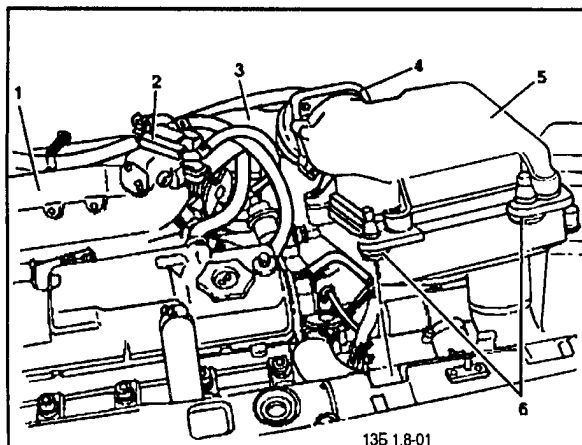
Система впуска воздуха (воздушный фильтр приподнят): 1 - ресивер; 2 - дроссельный патрубок; 3 - шланг впускной трубы; 4 - датчик массового расхода воздуха; 5 - воздушный фильтр; 6 - резиновые опоры воздушного фильтра
